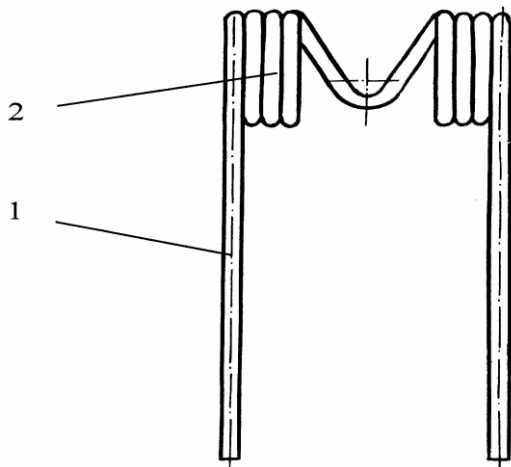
Пружинний зуб: 1 – зуб, 2 – пружина
